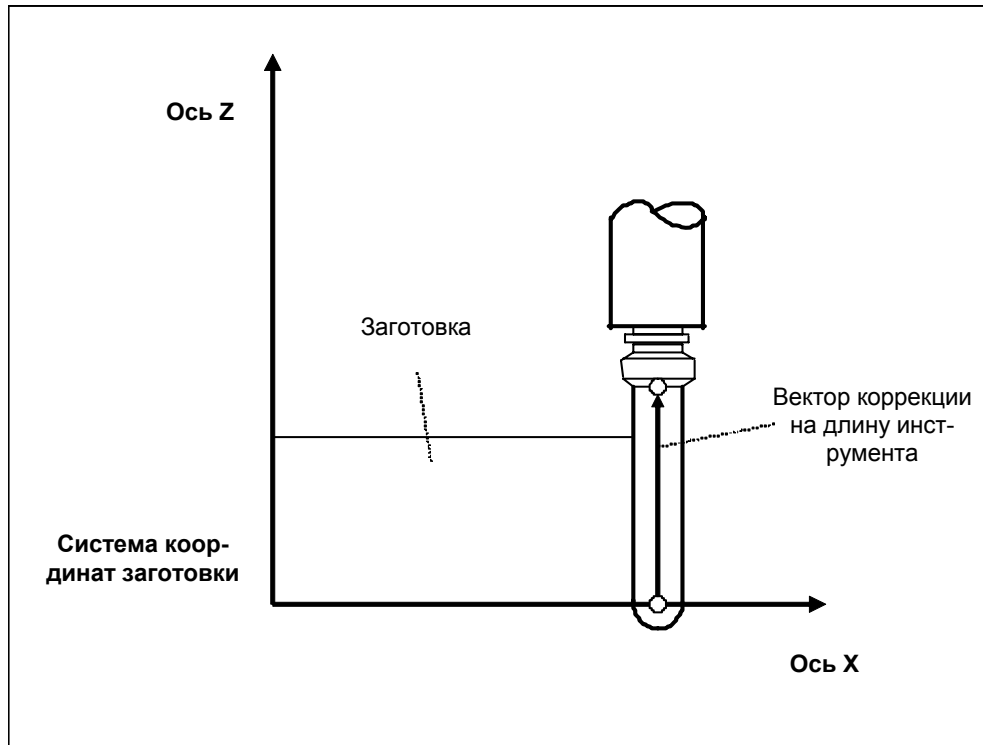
(q) Заготовка обрабатывается боковой стороной инструмента при отсутствии погрешности на установку заготовки
